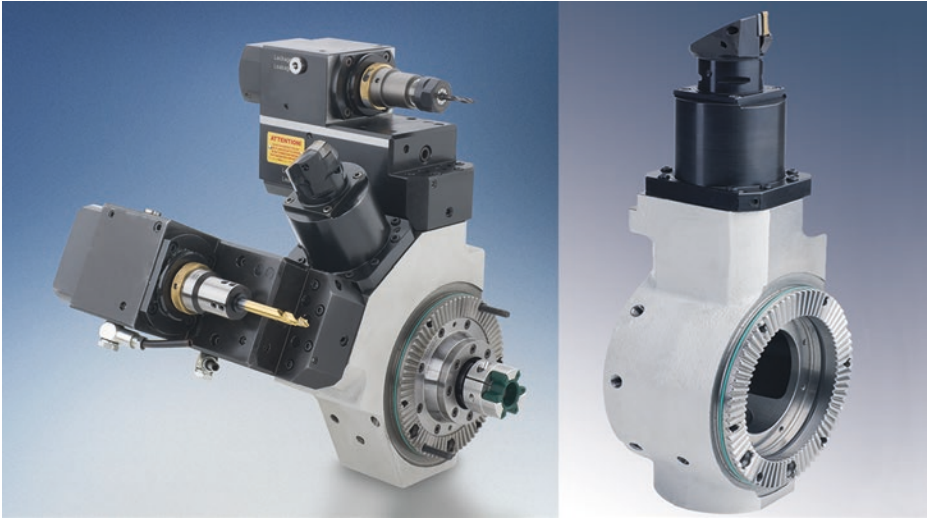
Mehrfach-Werkzeugkopf mit drei Werkzeugplätzen (links) und Einfach-Werkzeugkopf mit einem Werkzeugplatz (rechts), beide mit Verzahnungsschnittstelle zur Montage auf den Bearbeitungsstationen [Schu16a]
